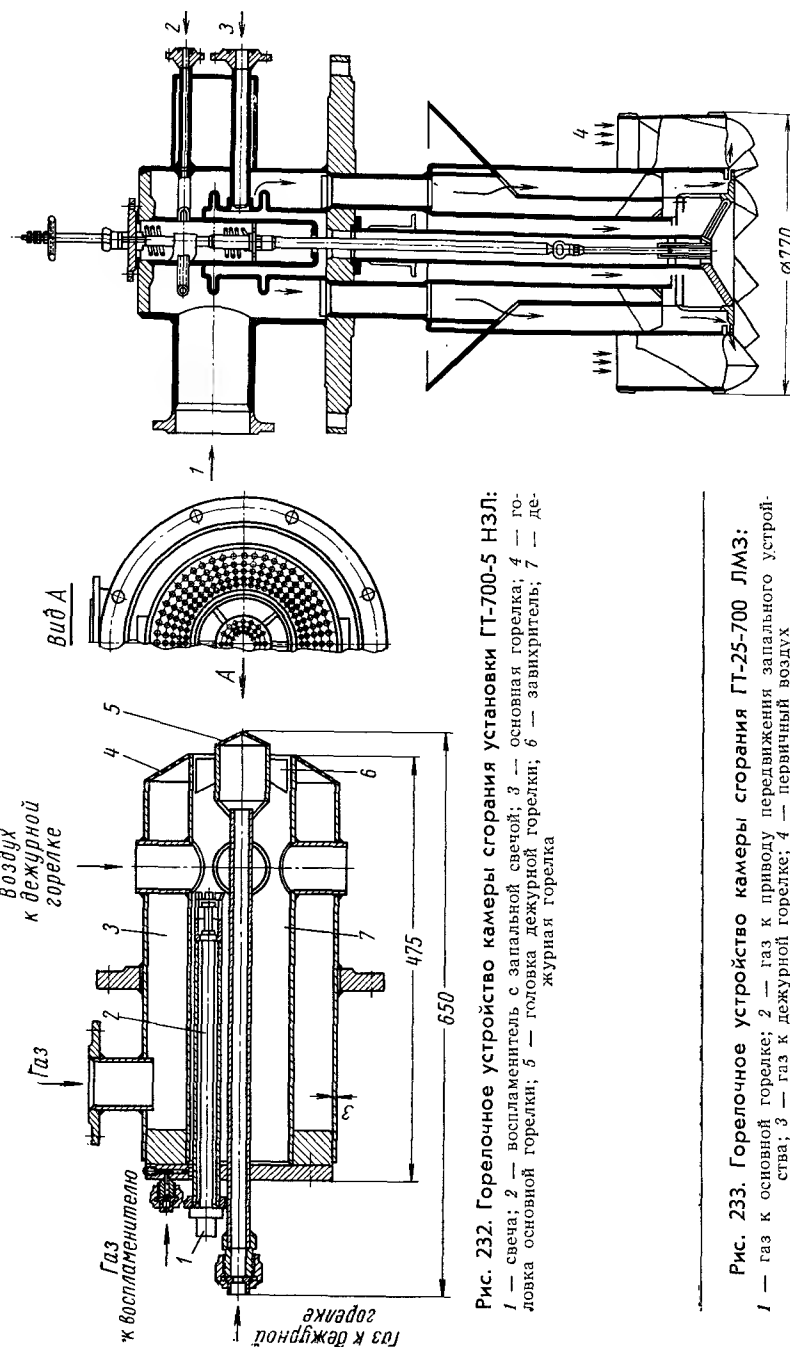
Горелочное устройство камеры сгорания установки ГТ-700-5 НЗЛ:
